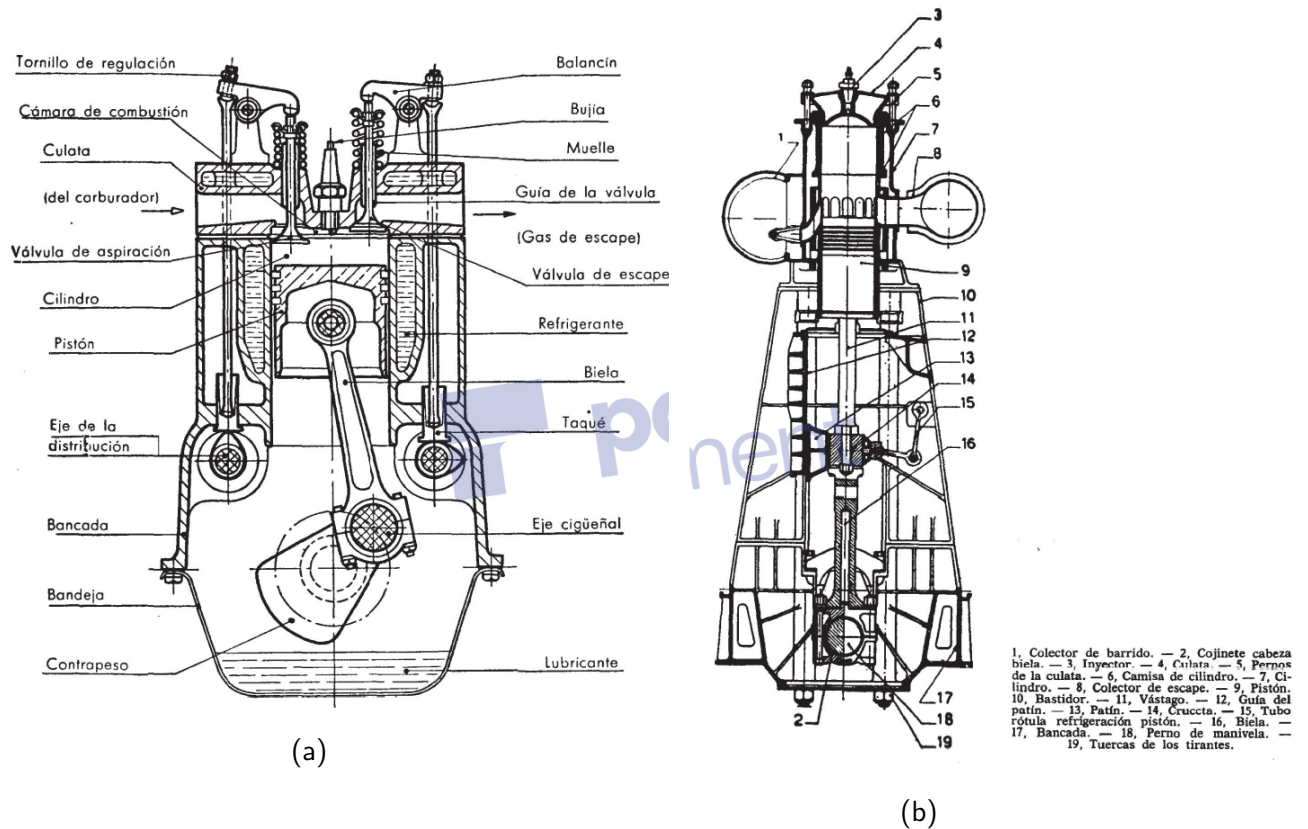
(a)Motor MECH, (b)Motor MEC. [1]
